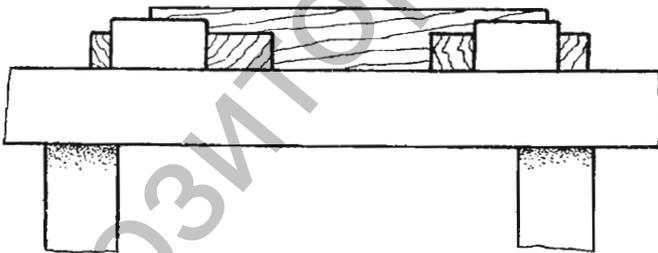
Крепление заготовки для резьбы при помощи клиньев.
